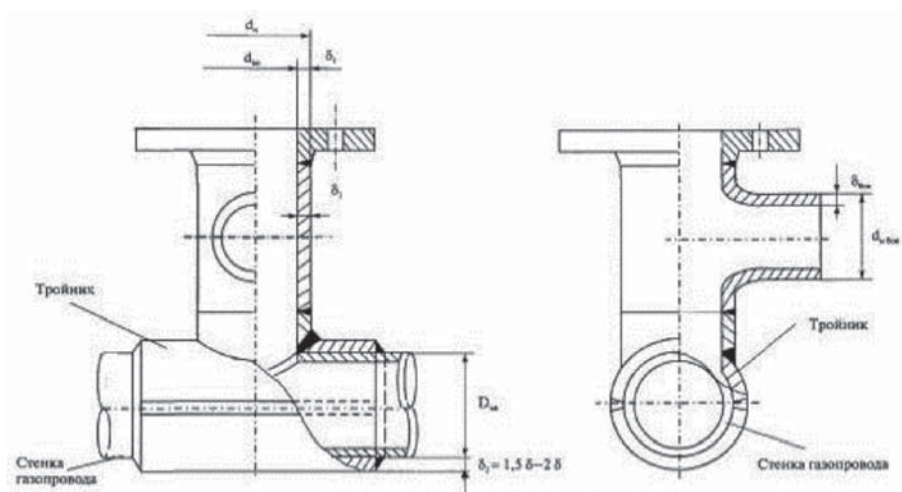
Разрезной тройник сварной с боковым ответвлением
